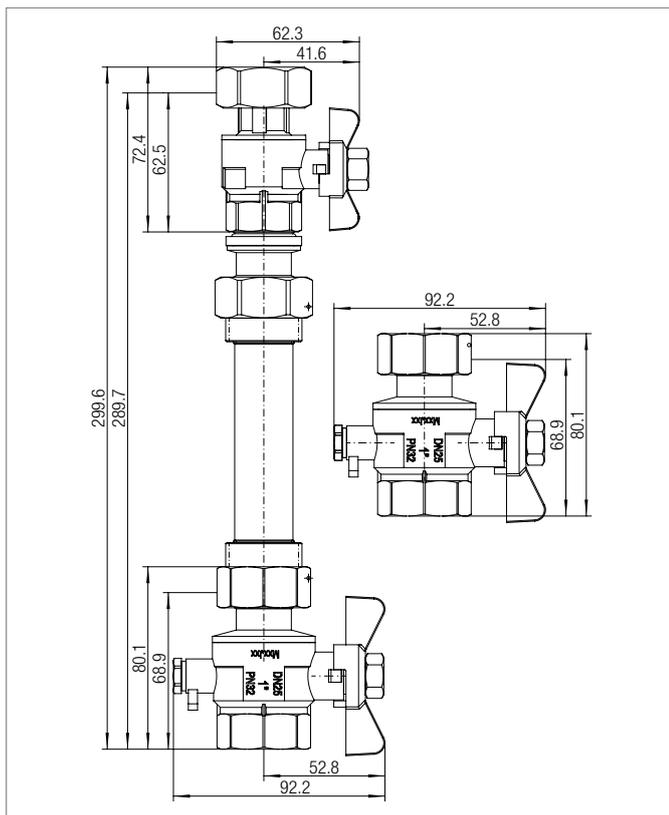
Dimensions kit de montage WMZ horizontal
